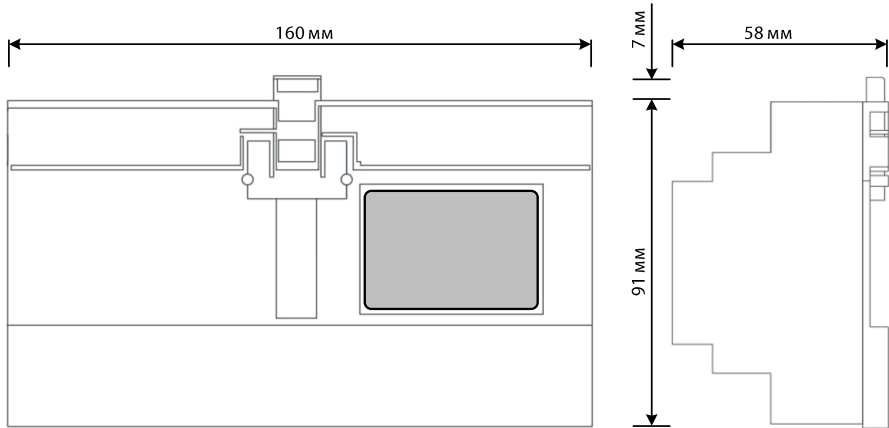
Габаритные и установочные размеры блоков ЛЕОН2.0.
